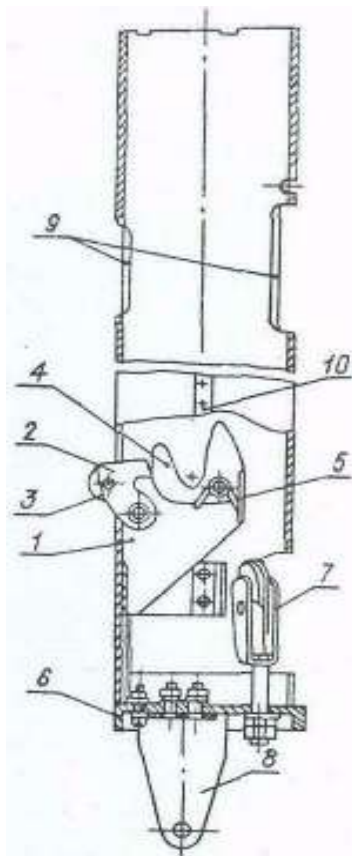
Подвижная секция: 1, 6 – корпуса; 2 – собачка; 3 – ролик; 4 – рычаг; 5 – пружина; 7 – блок; 8 – хвостовик; 9 – окна; 10 – шпонка
